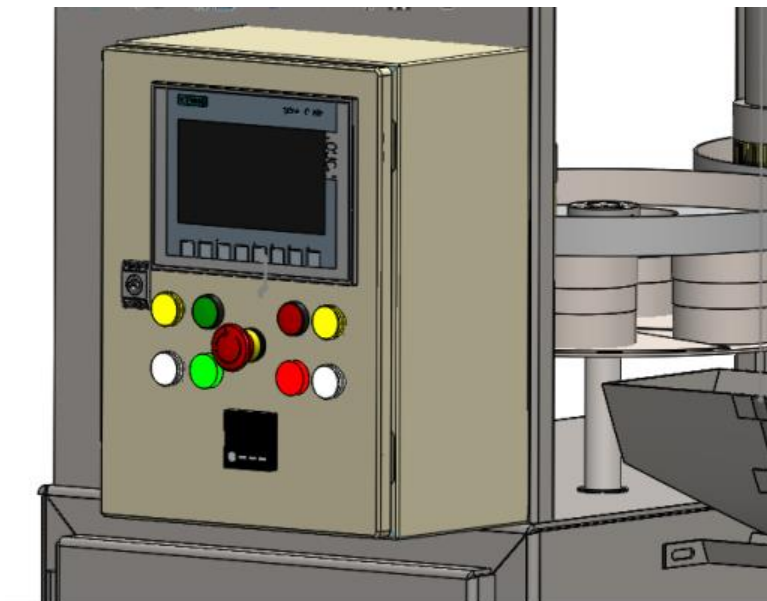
Montaje del GAB 1 en la máquina (elaboración propia).
